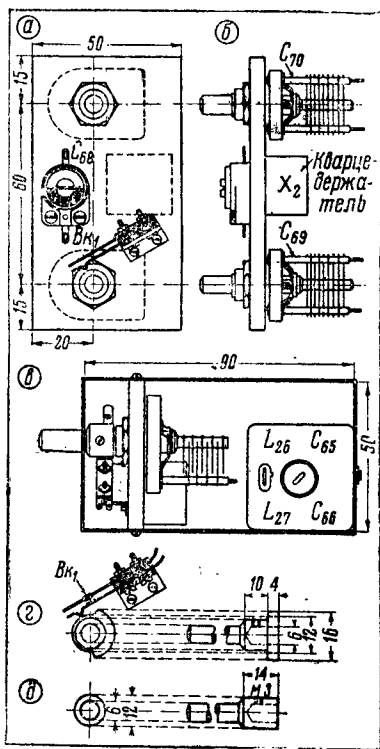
Кварцевый фильтр и его детали: а — расположение деталей фильтра на плате, вид сверху (удлинительные втулки сняты); б — то же, вид сбоку (удлинительные втулки и выключатель кварца сняты); в — вид на фильтр сверху; г — удлиняющая втулка для оси фазировочного конденсатора  $C_{69}$  и выключатель кварца; д — удлиняющая втулка для оси конденсатора связи  $C_{70}$
